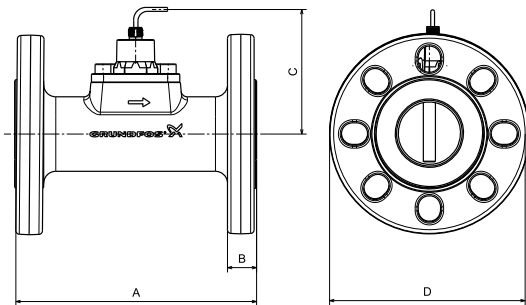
Abmessungen des VFI-Sensors mit Flanschen
